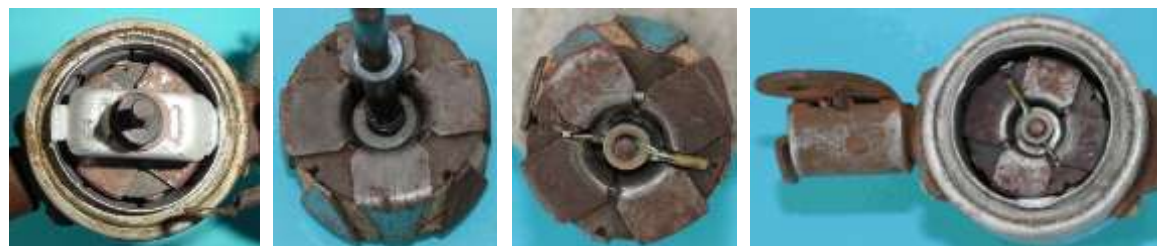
Anker: a) Kabelanschlussbolzen mit Kontaktsteg, b) Stirnansicht auf der Reibradseite, c) Spulenanschlüsse mit Bürste, d) Anker im Gehäuse
